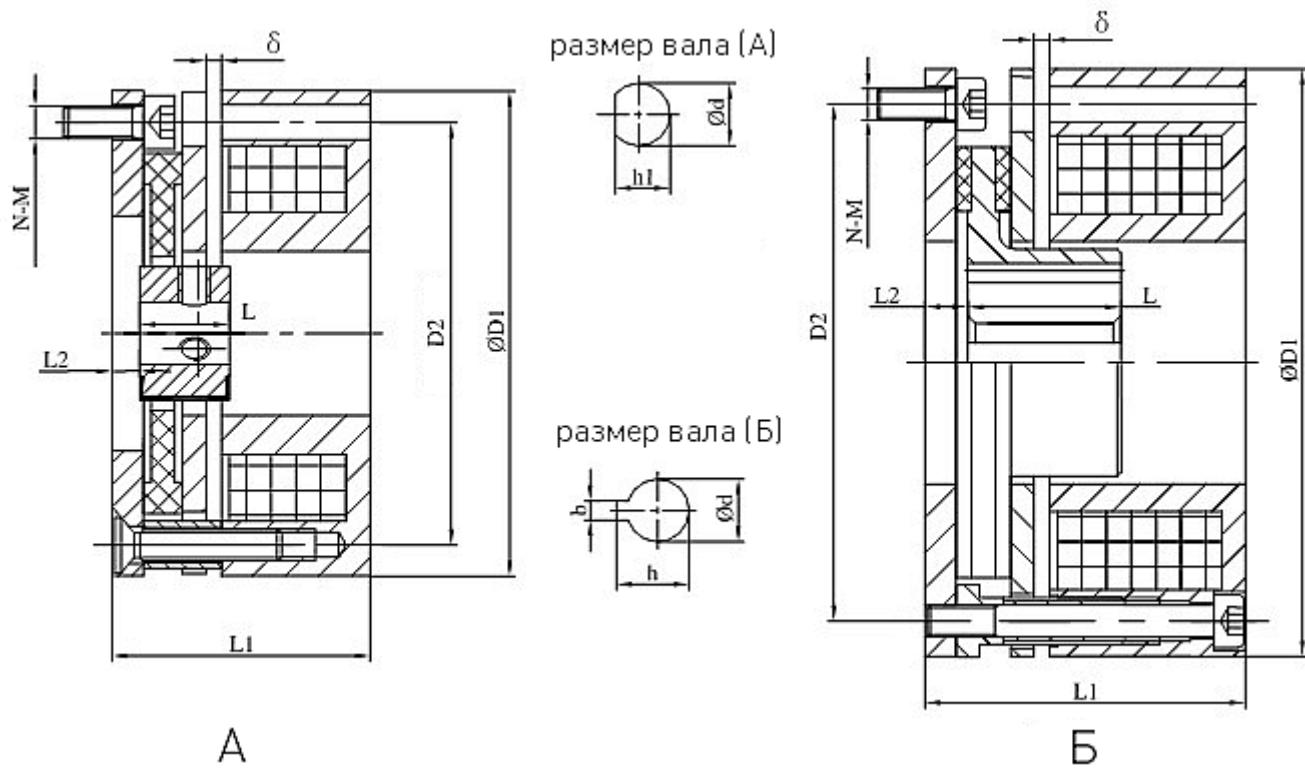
Габаритные и присоединительные размеры электрического тормоза
